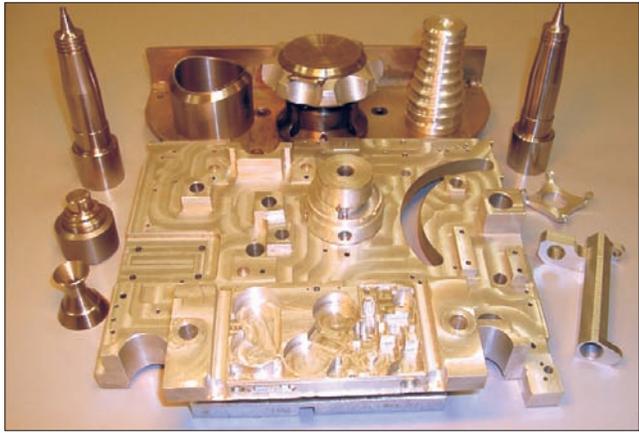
Детали после фрезерной и токарной обработки на станках с ЧПУ
